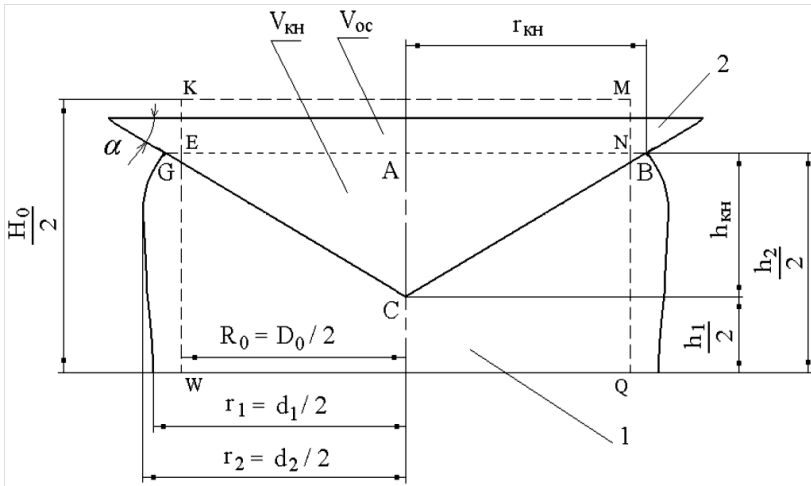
Осаджування заготовок кінчними бойками (верхня частина) [99]
